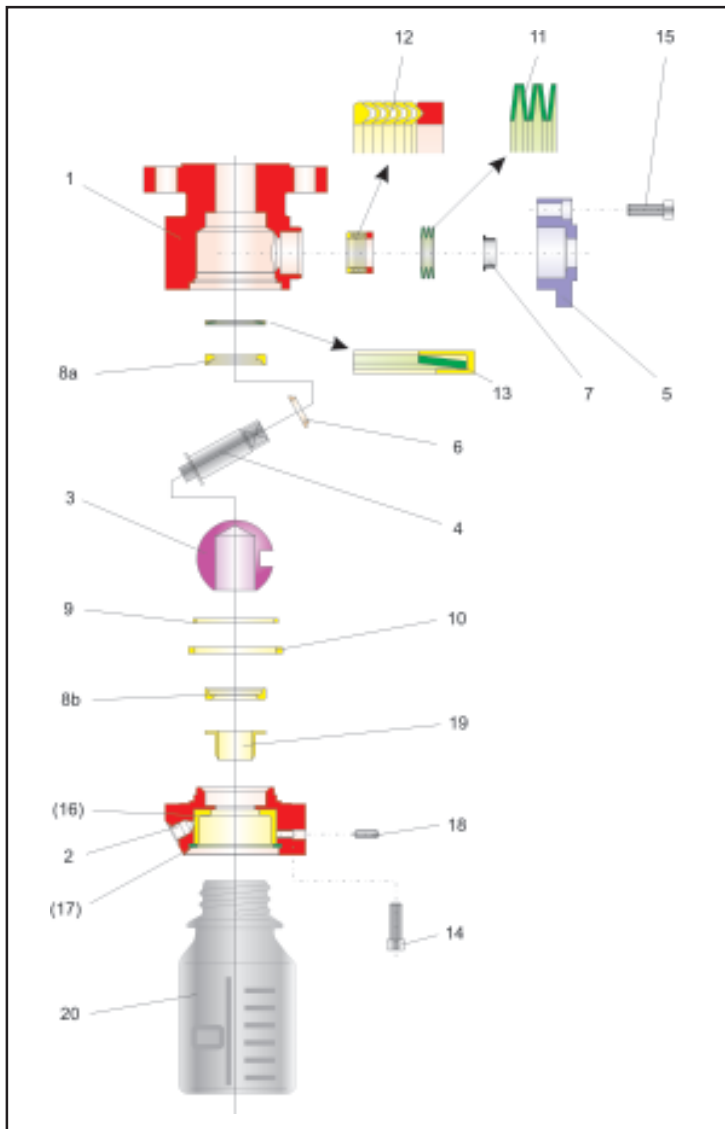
Explosionszeichnung des Probenehmerhahns BR 27i
